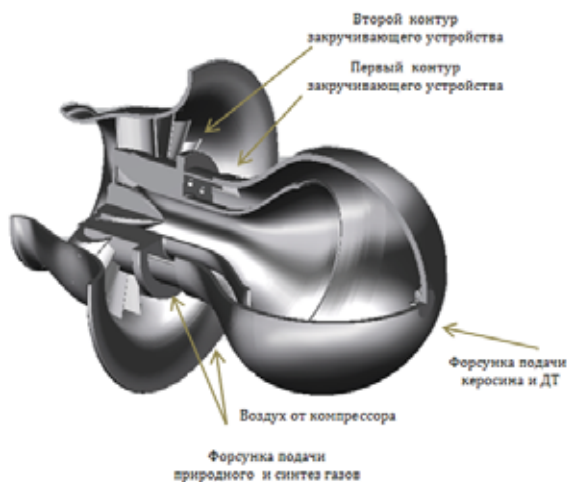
Конструктивная схема многотопливного противоточного горелочного модуля
